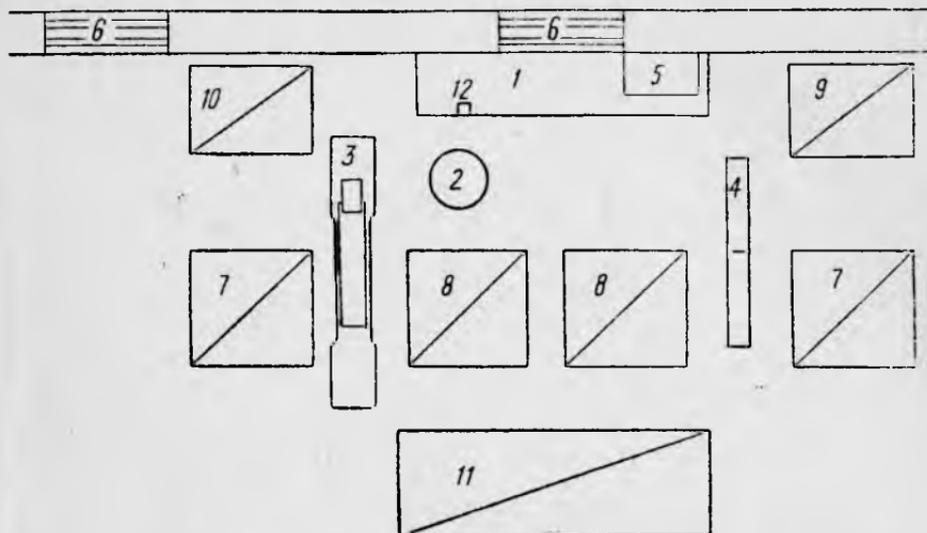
Расположение приспособлений и материалов на рабочем месте: 1—верстак, 2—«чурбан», 3—бондарная скамья, 4—бондарный фуганок, 5—шкаф для инструментов (над верстаком), 6—окна, 7—места для необработанной клепки, 8—места для обработанной клепки, 9—место для остовов, 10—место для доньев, 11—место для готовых изделий, 12—наковальня
